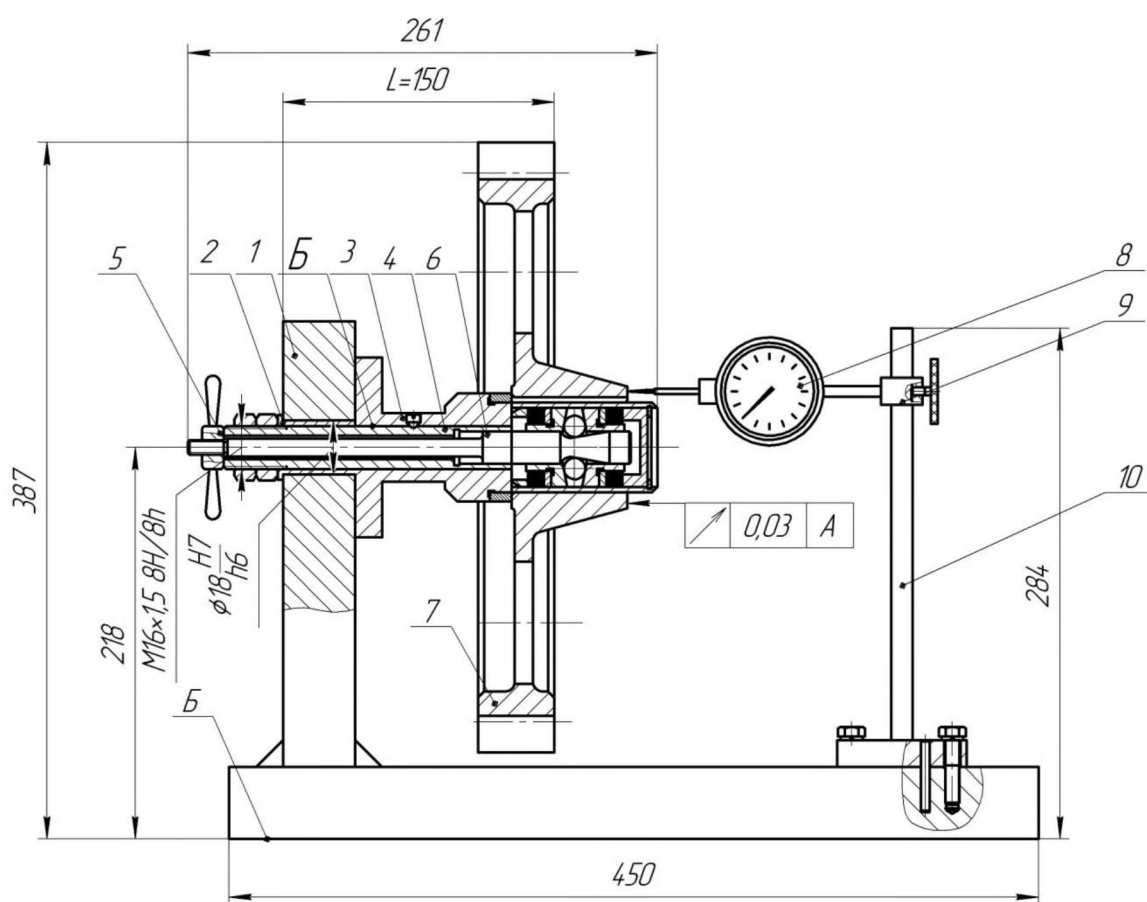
Пристосування для контролю торцевого биття деталі
